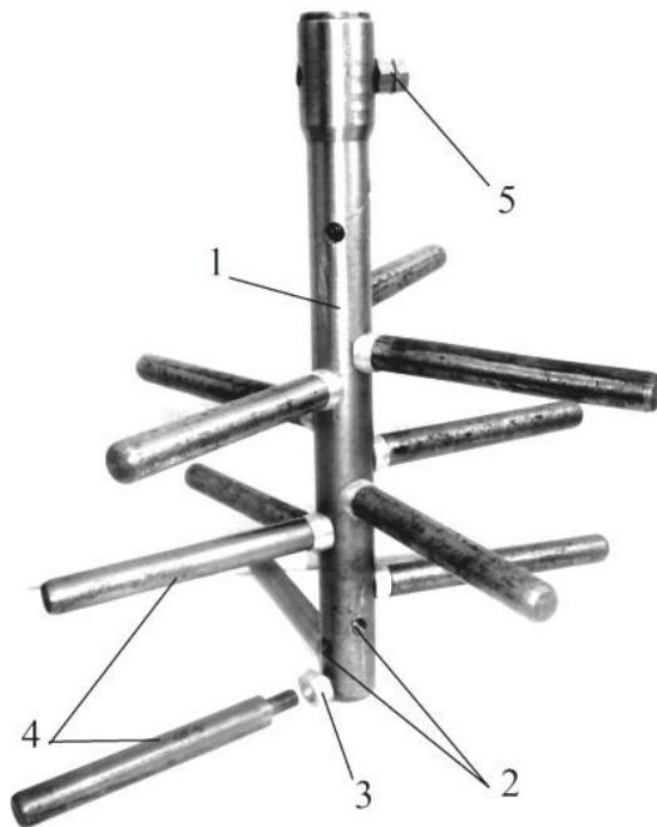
Загальний вигляд об'ємно-гвинтового робочого органу: 1 - робочий вал; 2 - отвори для установки лопатей; 3 - посадкова втулка; 4 - тістомісильна лопать; 5 - фіксатор робочого вала на приводному валу
